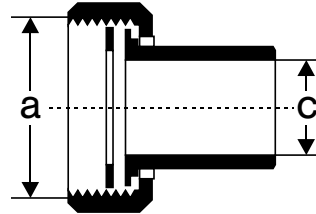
Verschraubung mit Schweißverbindung
